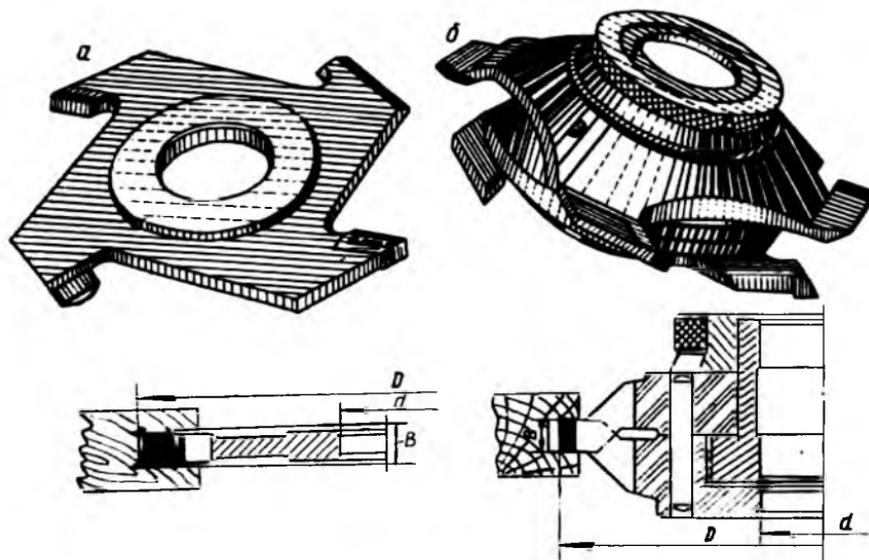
Общий вид и конструкции фрез для выборки пазов:
